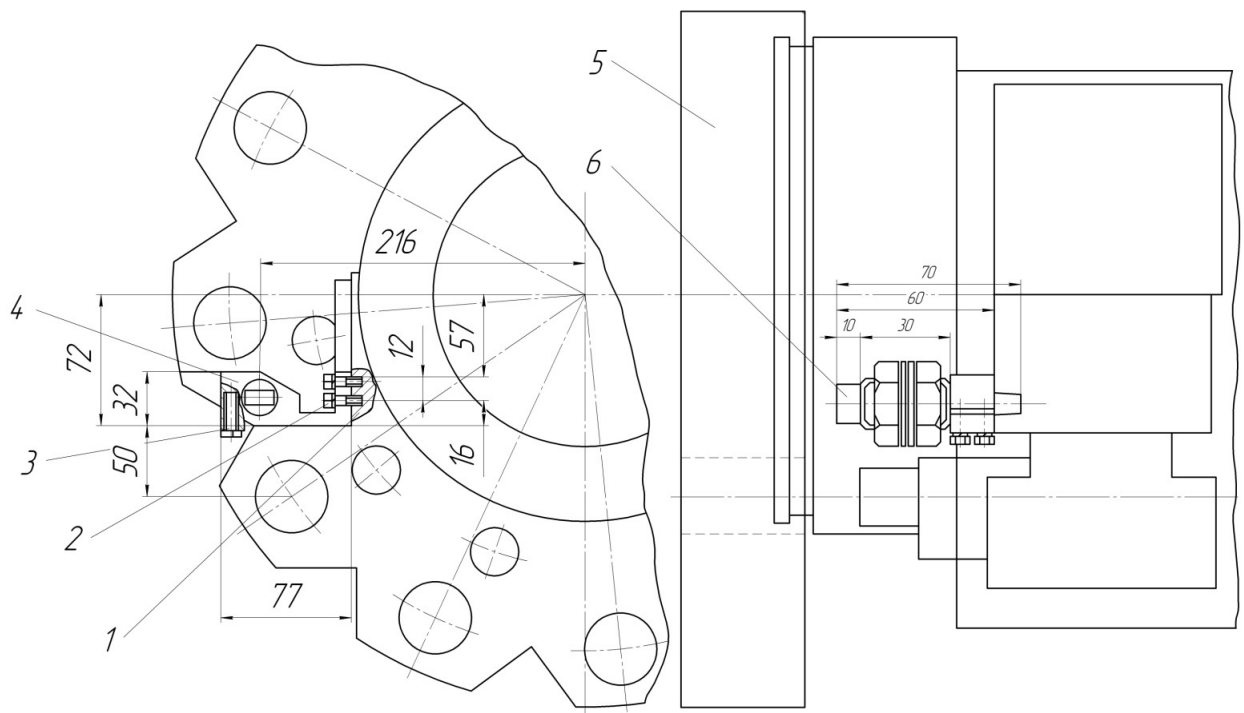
Схема розміщення індуктивного датчика на револьверному супорті верстата 1П420ПФ40
